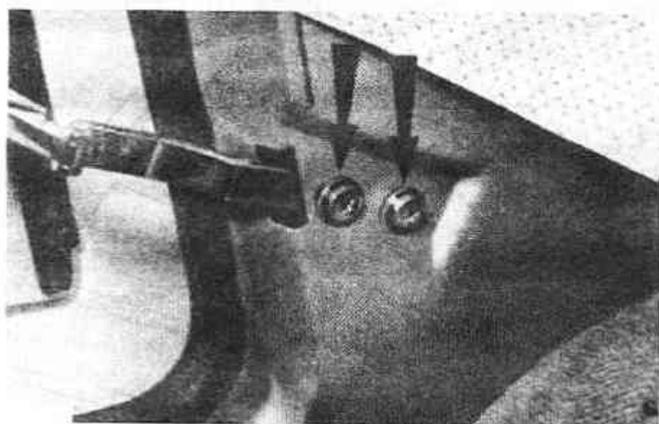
Выверните винты защелки открывающейся форточка (Разд.23)
